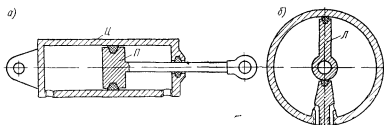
Пневматические исполнительные элементы: а — с поступательным движением поршня, б — с вращательным движением поршня
